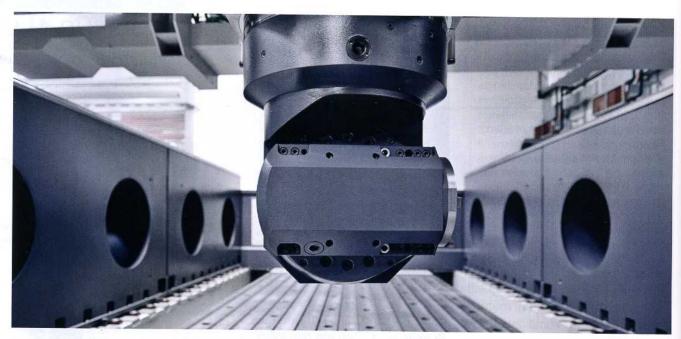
SHW Werkzeugmaschinen hat den Maschinenständer einer hauseigenen UniForce Maschine von der Vertikalen in die Horizontale gelegt und daraus eine interessante Portalfräsmaschine entwickelt
